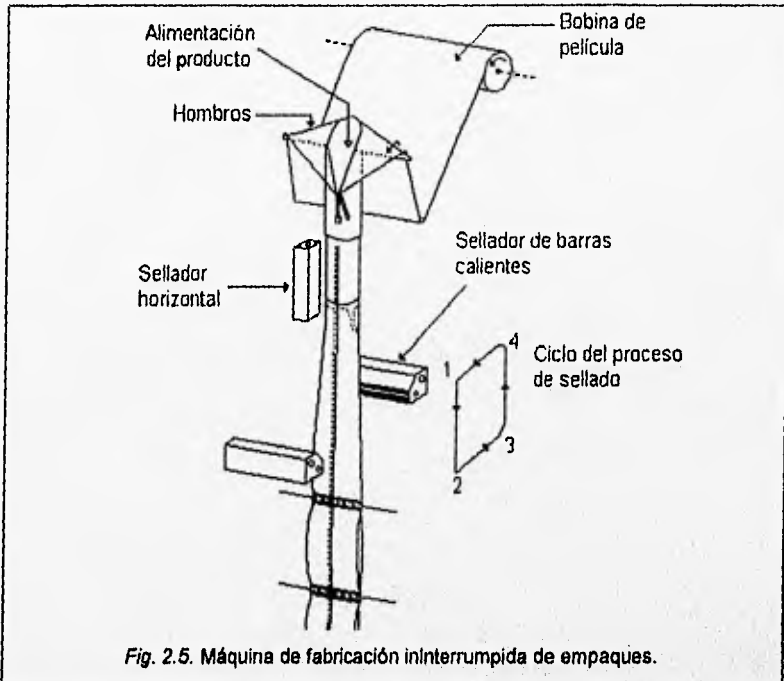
Máquina de fabricación ininterrumpida de empaques.
